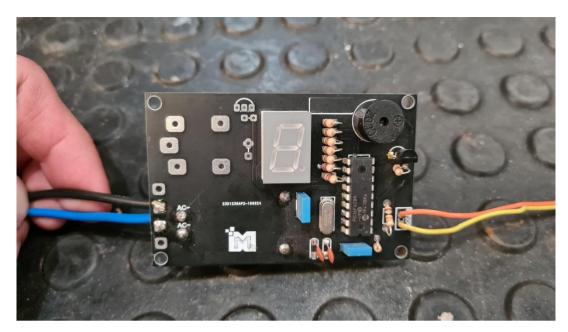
Placa montada com todos os componentes. Fonte: Autor
